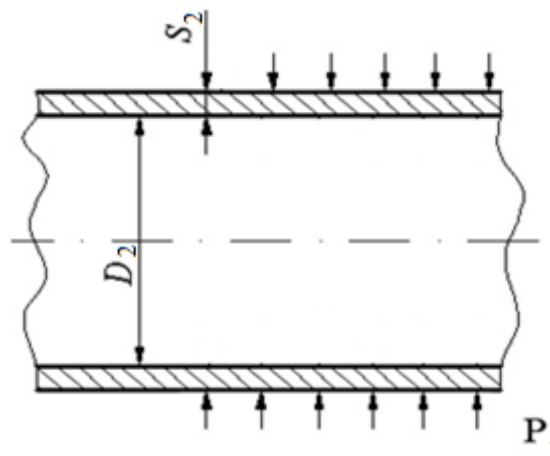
Розрахункова схема внутрішньої труби
